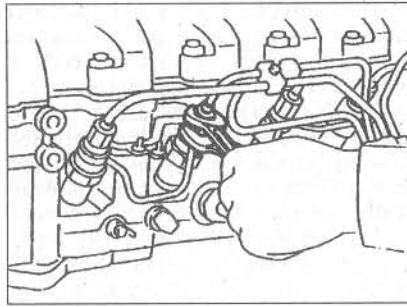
Откручивание форсунки из головки блока цилиндров (Глава 37)
